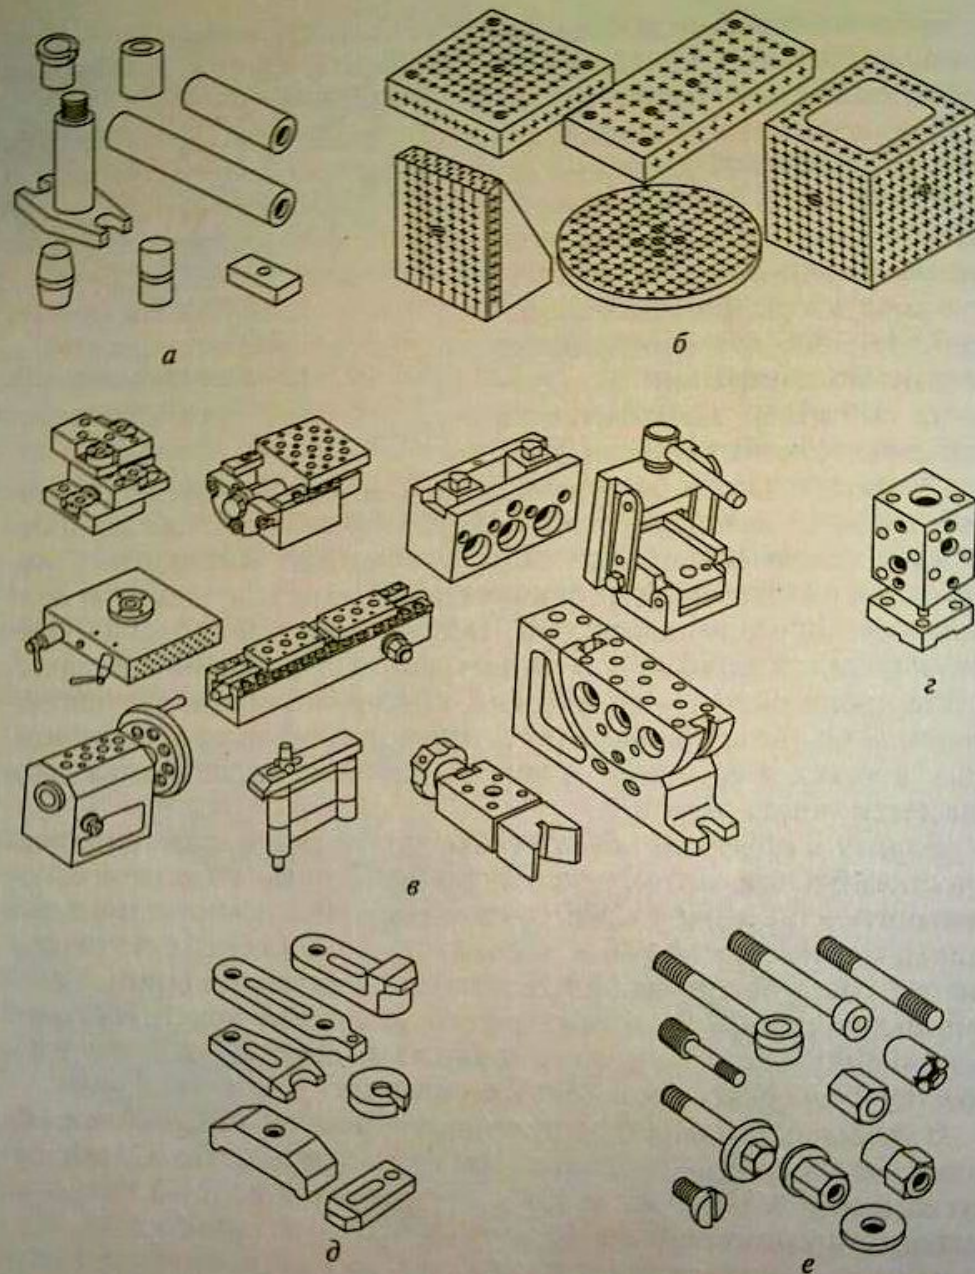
Базовый набор деталей и сборочных единиц универсально-сборных приспособлений:
